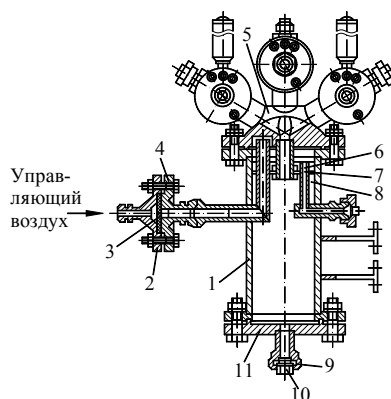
Прибор постоянного давления установки: 1 – корпус фильтра; 2 – крышка клапана; 3 – мембрана; 4 – корпус клапана; 5 – блок камер сгорания; 6 – сливной патрубок; 7 – механический дисковый фильтр; 8 – вода; 9 – гайка; 10 – заглушка; 11 – крышка фильтра.
